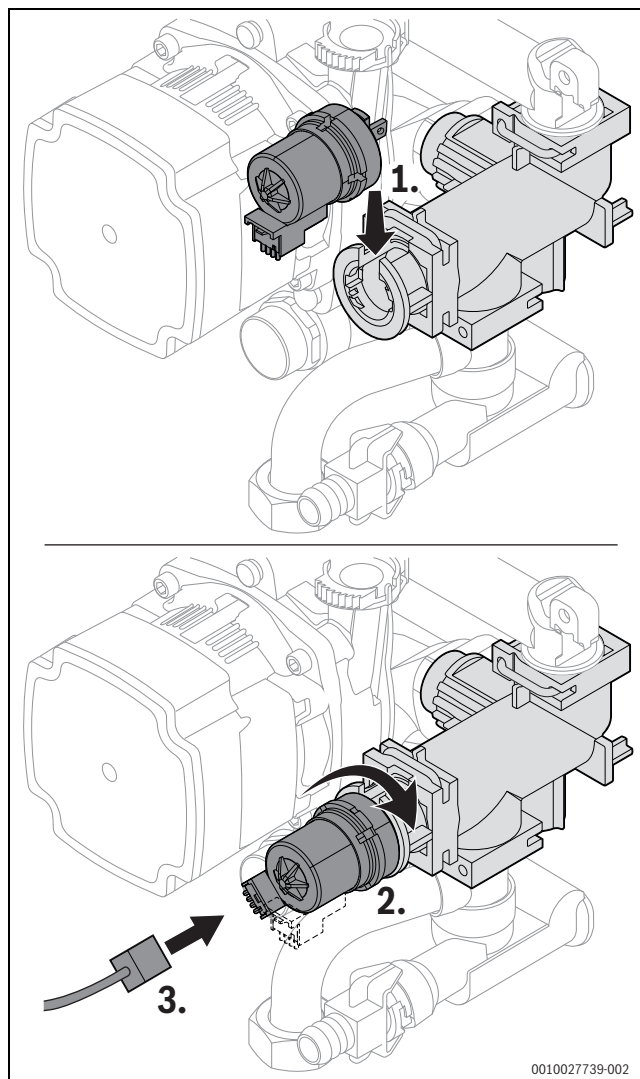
Montar el motor de la válvula de 3 vías (variante sin tornillos)
